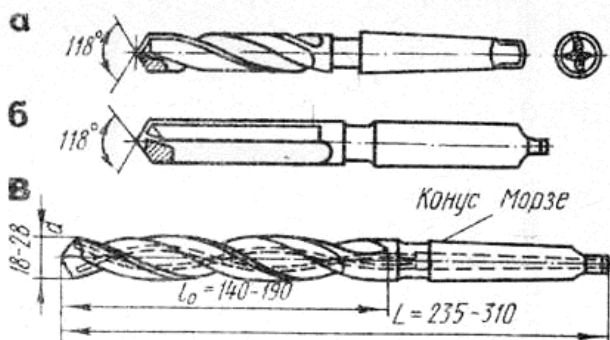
Сверла, оснащенные пластинками из твердого сплава с винтовыми (а), прямыми (б) канавками, каналами для охлаждающей жидкости (в)
